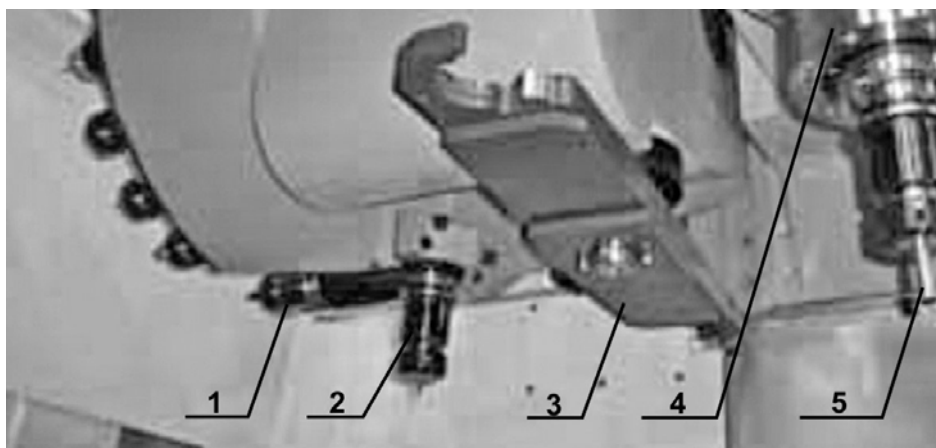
Механизм типа «РУКА» (вид со стороны манипулятора):
